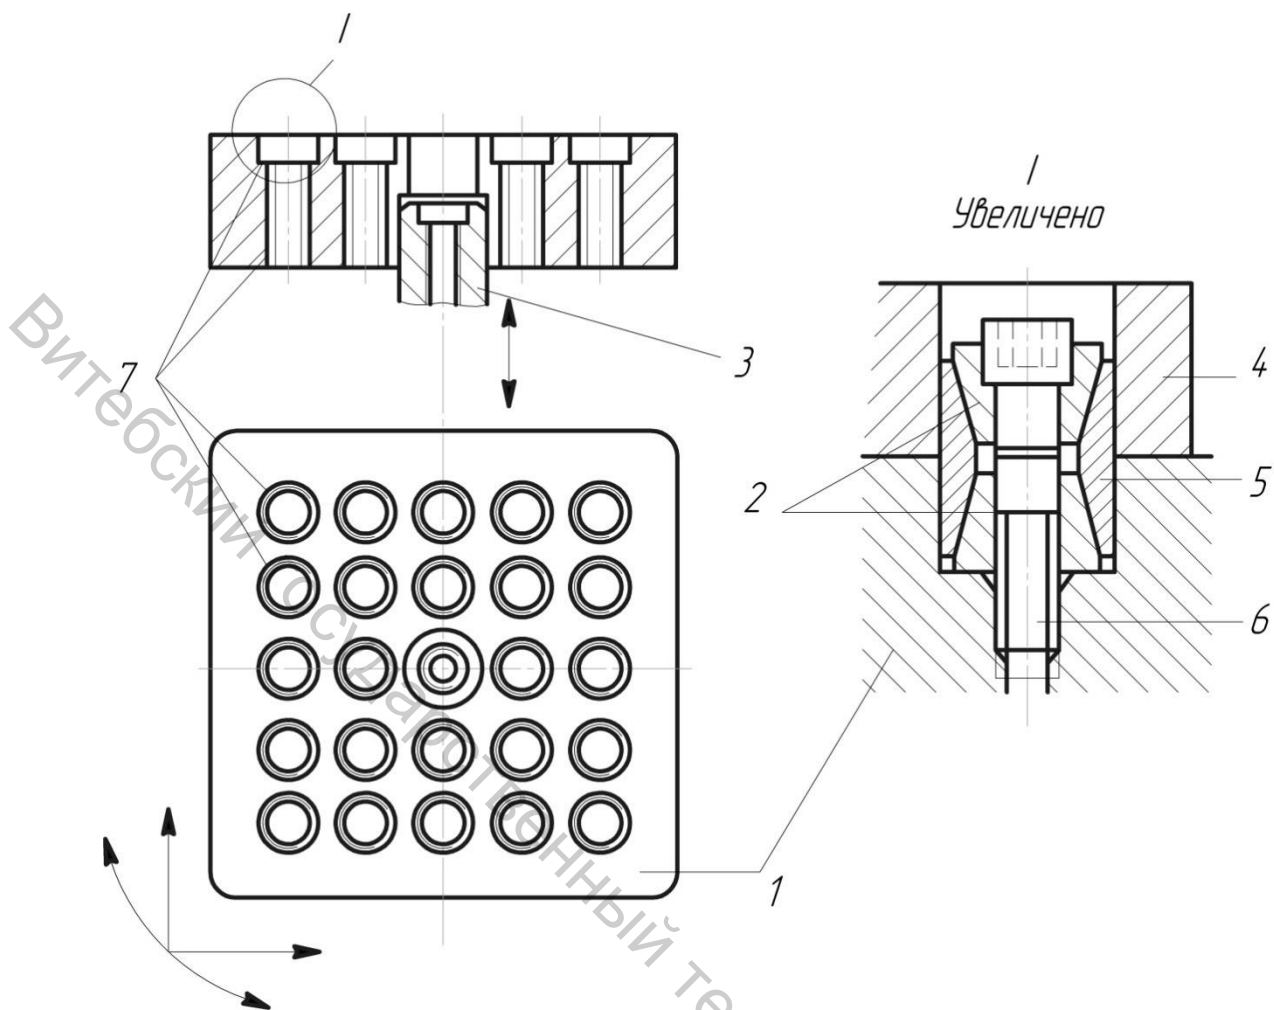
Стол многооперационного фрезерно-сверлильно-расточного станка с линейной и круговой подачами (1 – цанговая втулка беззазорного базирования приспособлений)
